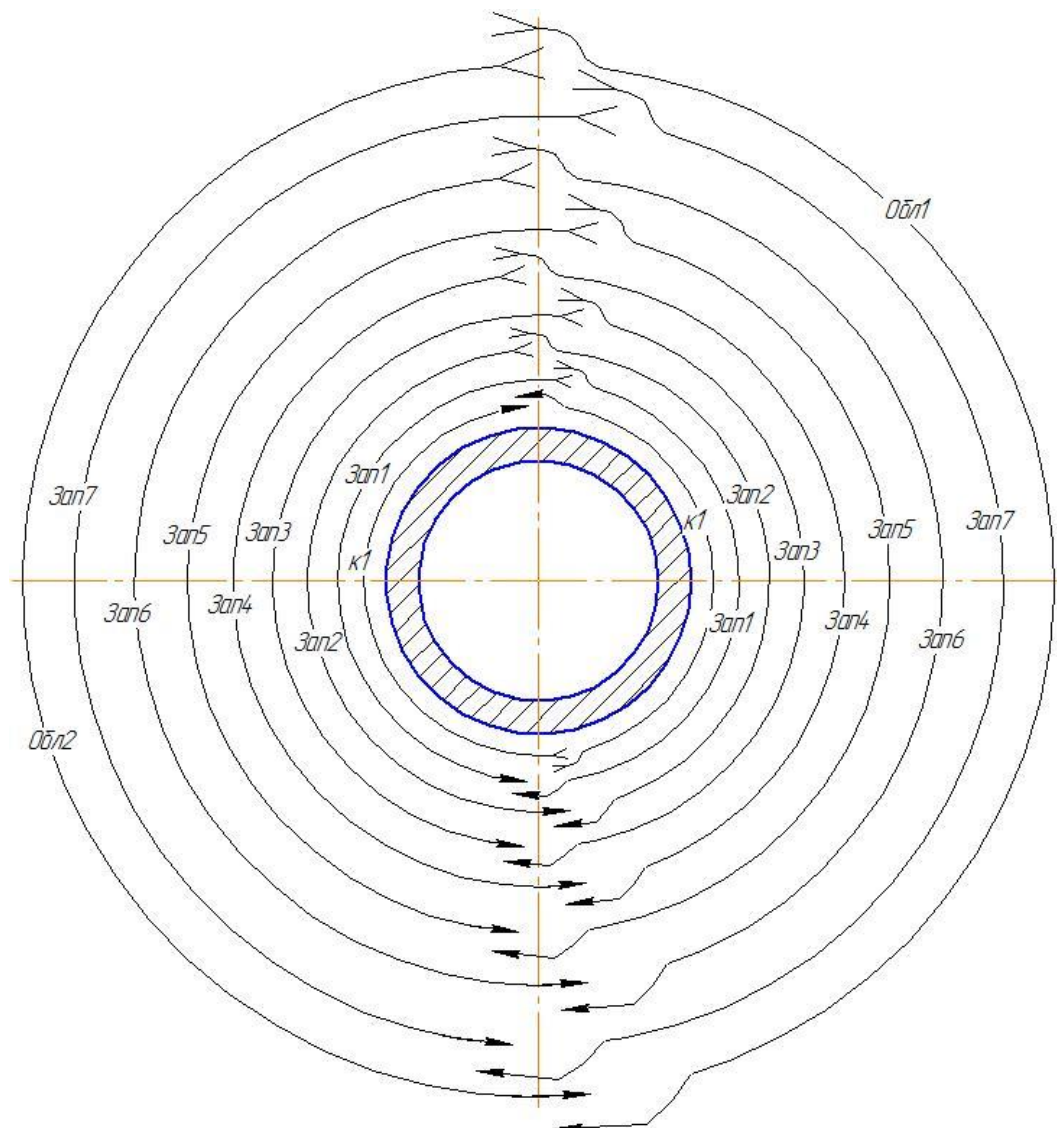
Схема полуавтоматической сварки порошковой проволокой
